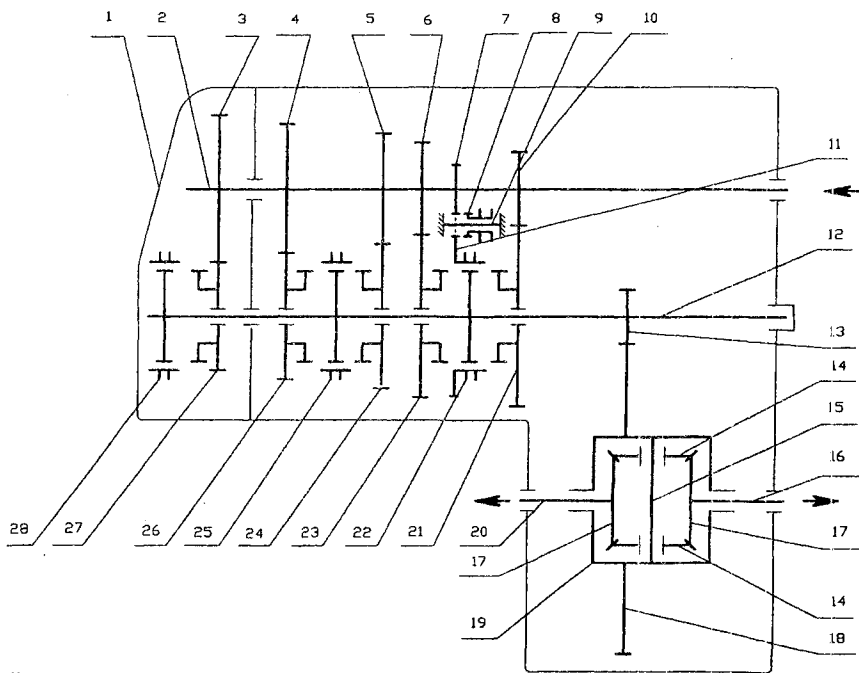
Кинематическая схема двухвальной пятиступенчатой коробки передач с главной передачей автомобиля ВАЗ-2110:
